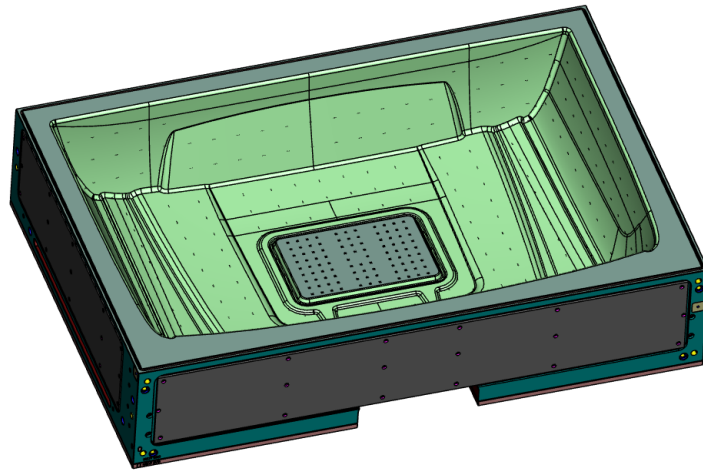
CAD-Daten des Tiefziehwerkzeuges
